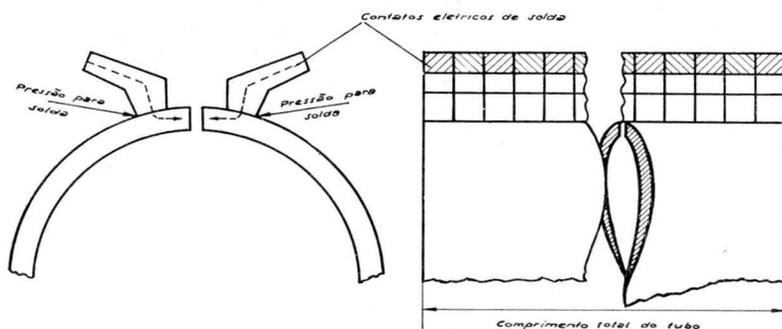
Solda de topo por caldeamento elétrico, para tubos  $\varnothing$  500 mm a 1400 mm, em grandes séries.
